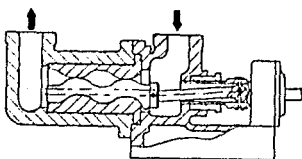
BOMBA DE TORNILLO DE ROTOR SIMPLE
